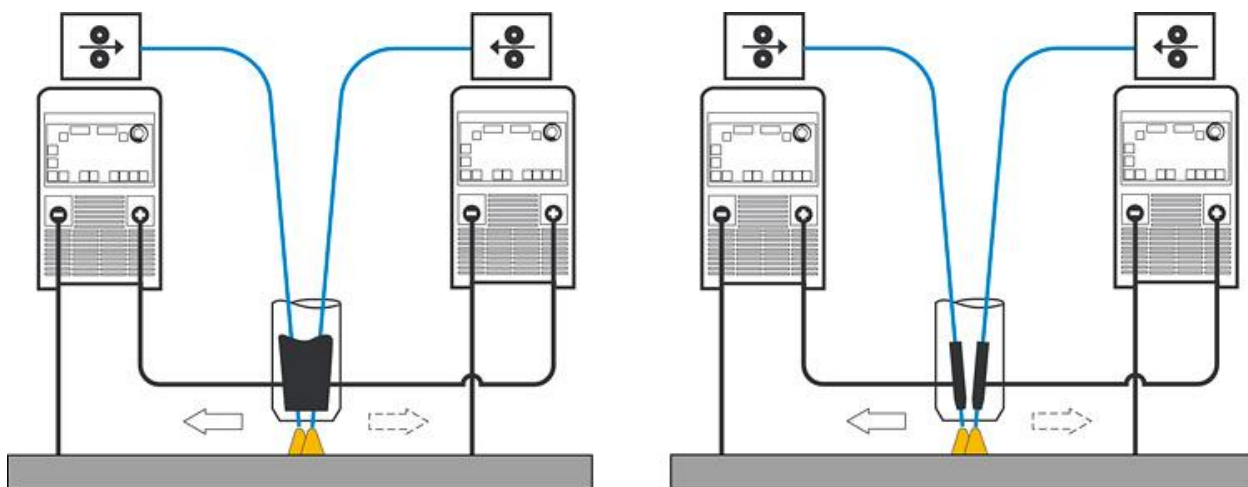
Сварка двумя проволоками с общим контактным наконечником (слева) и тандемная сварка (справа)
